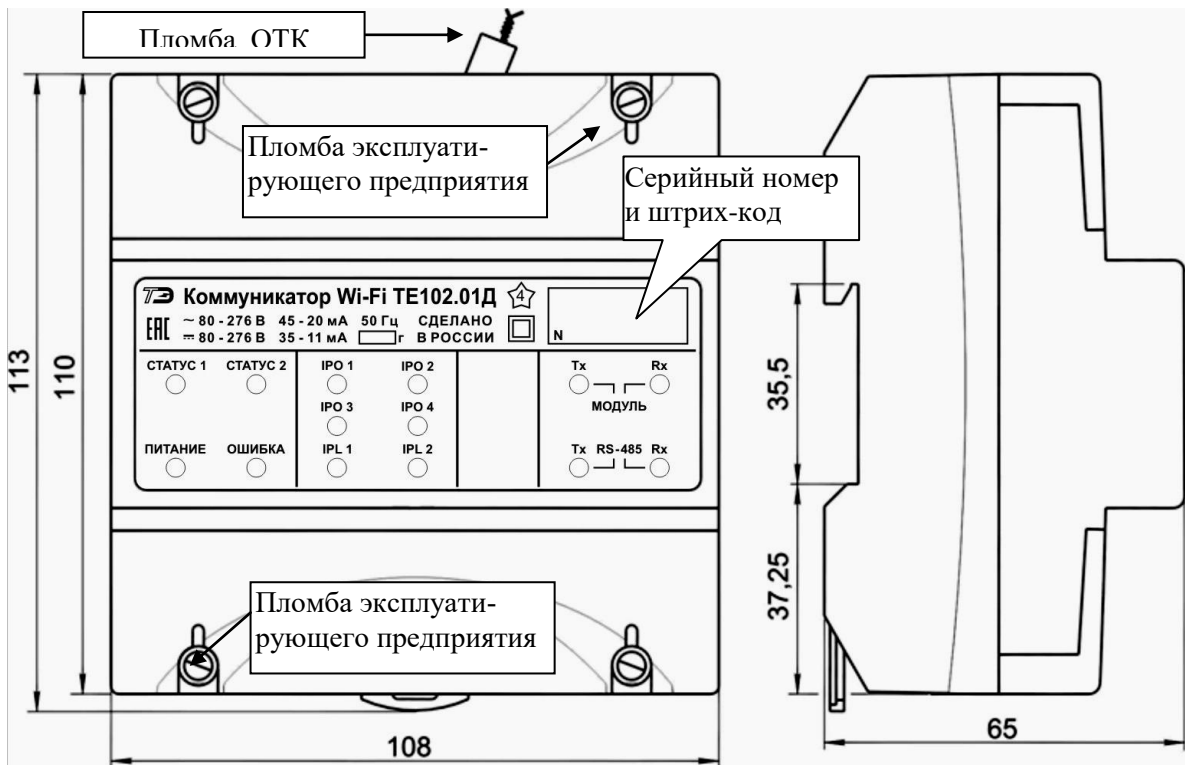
Габаритный чертеж и установочные размеры коммуникатора Wi-Fi TE101.02Д с защитными крышками
